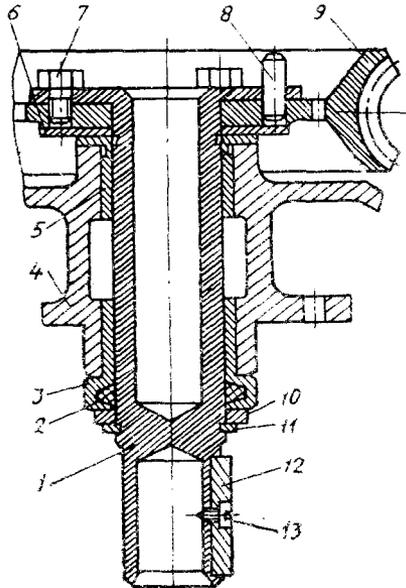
Установка червячной шестерни в редукторе аэропыла:
